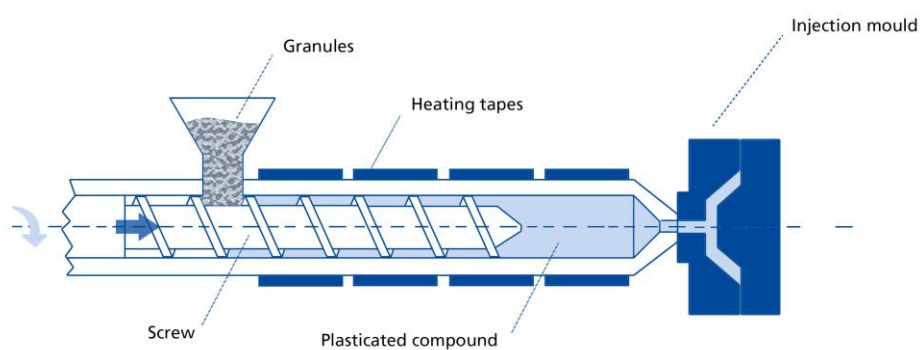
Componentes da moldação por injeção: (a partir da esquerda) fuso, grânulos, bandas de aquecimento, composto plastificado, molde [44]
